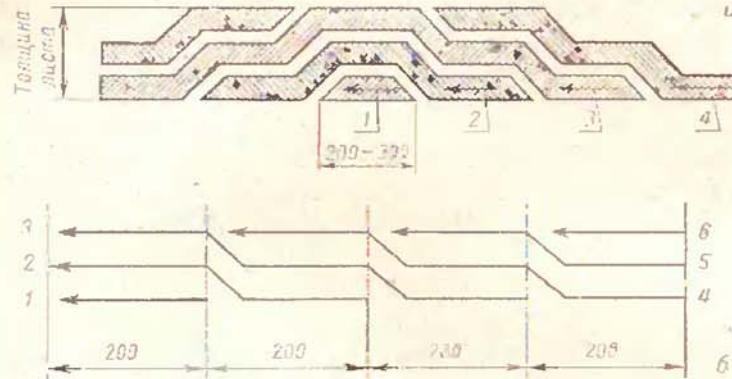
Схема сварки длинных многослойных швов:
